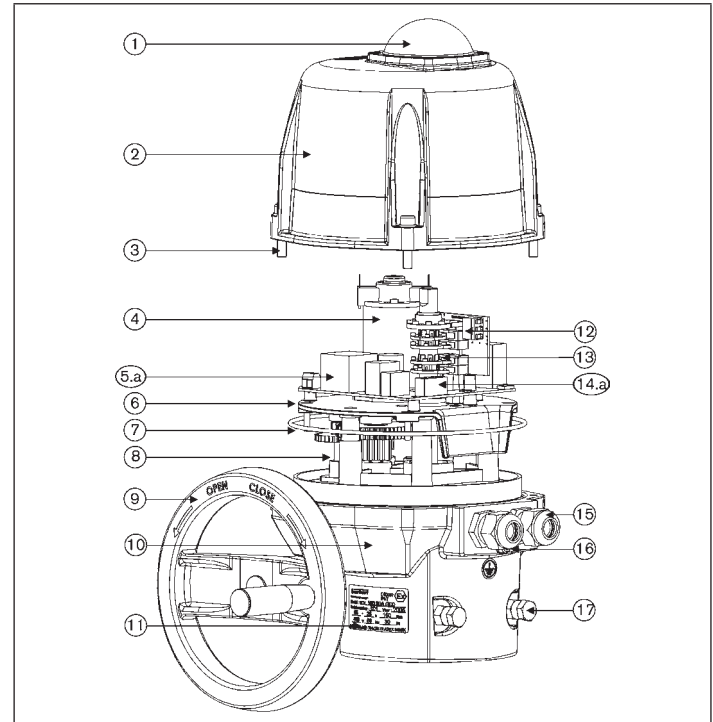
Explosionsdarstellung Motor 100 - 300 Nm
